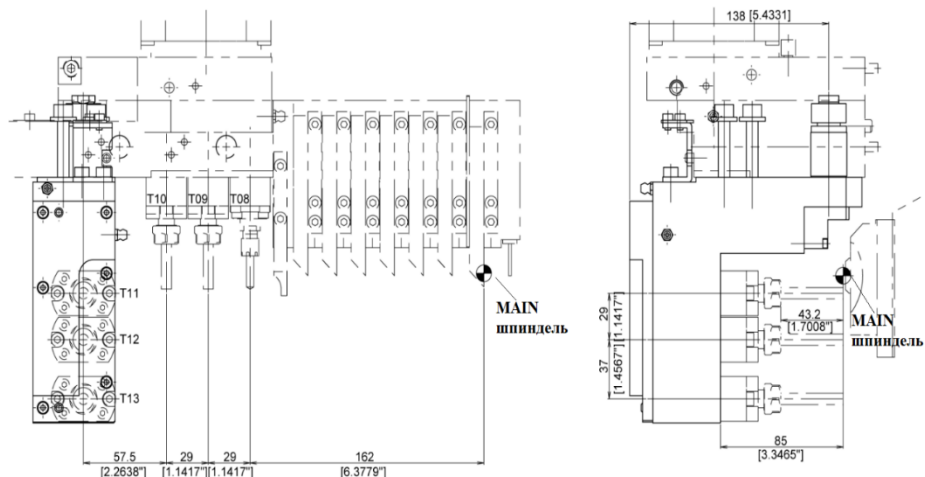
Кінематична схема комплектування верстата Sincom L12 2M10 для «MAIN шпиндель»
